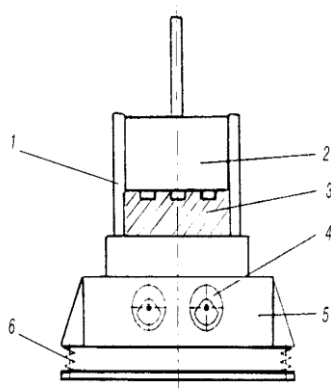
Вибромашина. Основные элементы конструкции:
